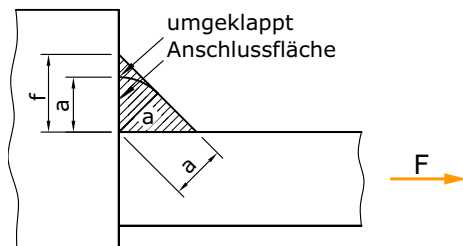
wsZ) Berechnung der Spannungen in einer Schweissnaht
